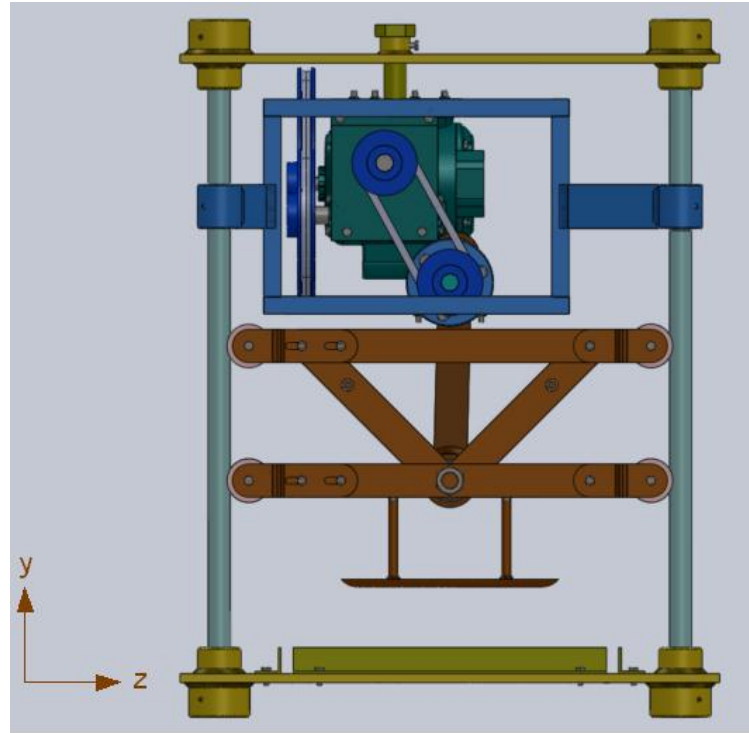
Equipo de ensayo ensamblado (vista lateral izquierda).
